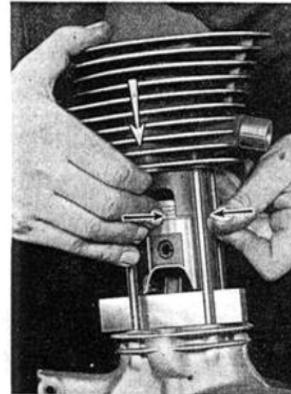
Aufschieben des Zylinders; Kolben auf Holzleiste auflegen, Ringe in Ringnuten eindrücken, so daß Ringenden an den Sicherungsliften liegen
